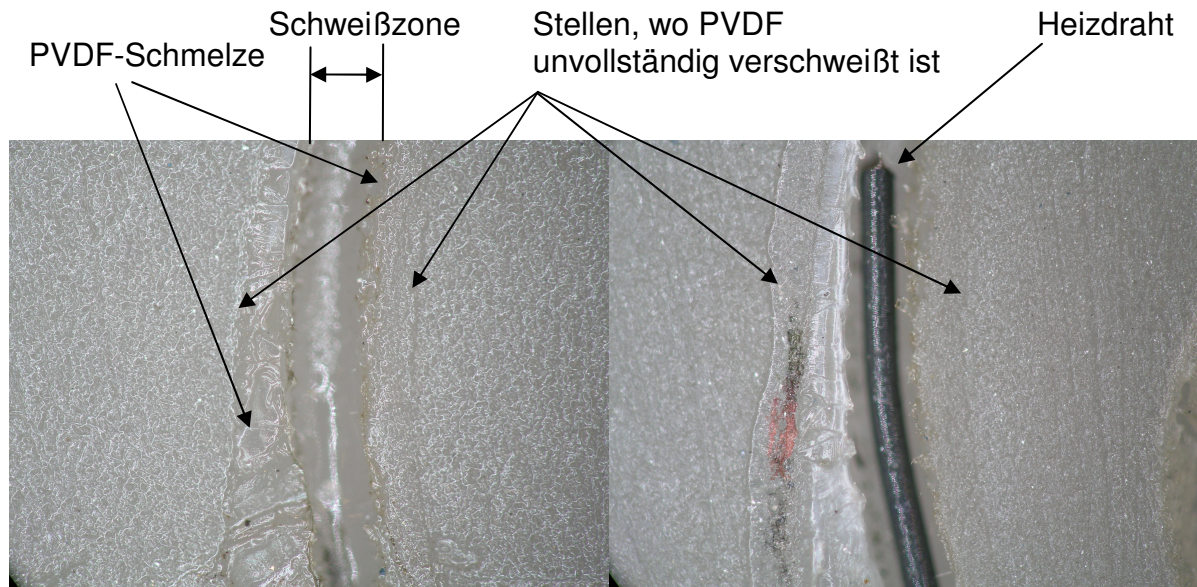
Schweißzone im Gehäuse (links) und im Gehäuse mit Heizdraht (rechts).
